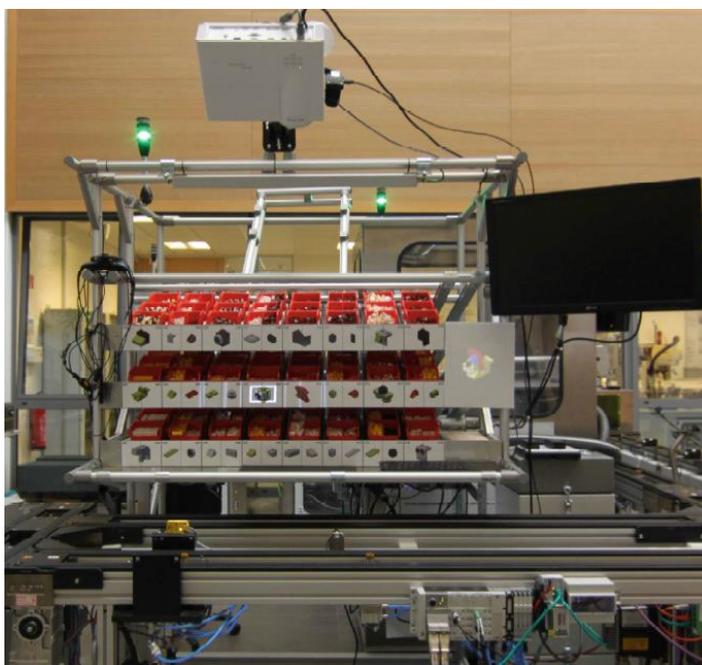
smARt.Assembly* - Sistema híbrido de Montagem Inteligente [3]
